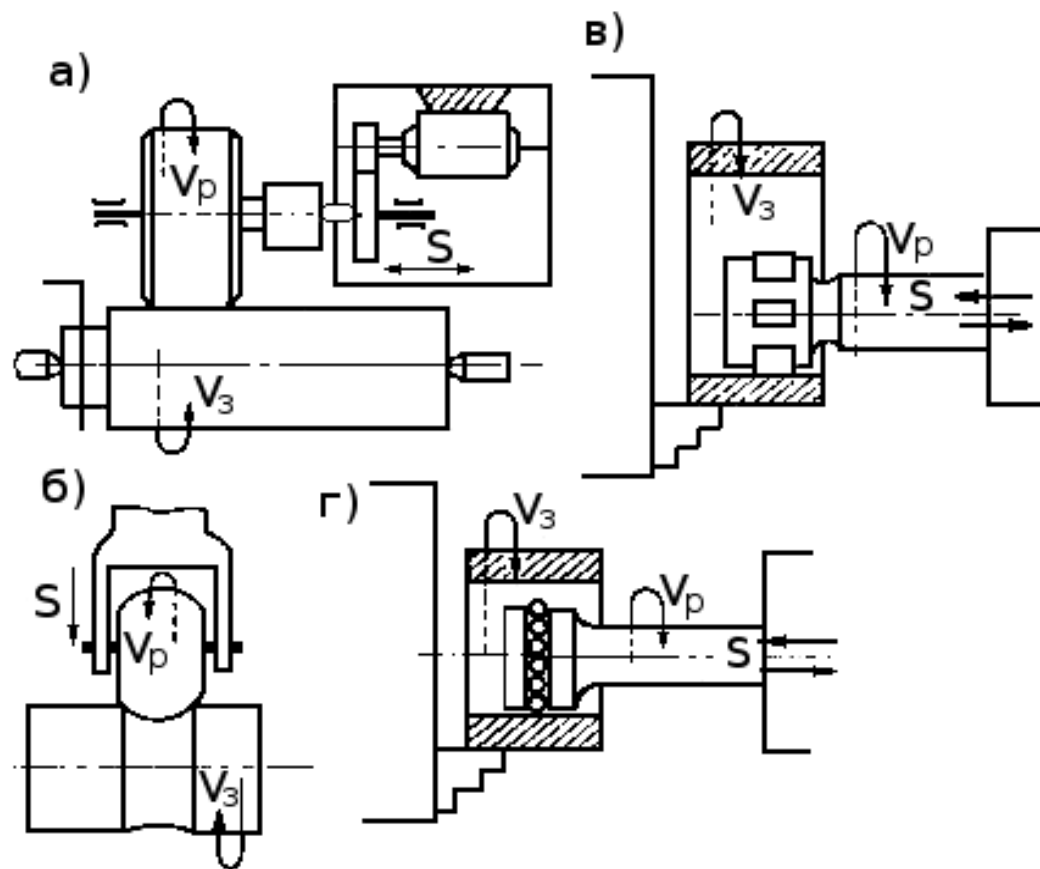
Обкочування та розкочування поверхонь деталі: а – обкочування циліндричної поверхні; б – обкочування фасонної поверхні; в – розкочування внутрішньої поверхні роликами; г – розкочування внутрішньої поверхні шариками
